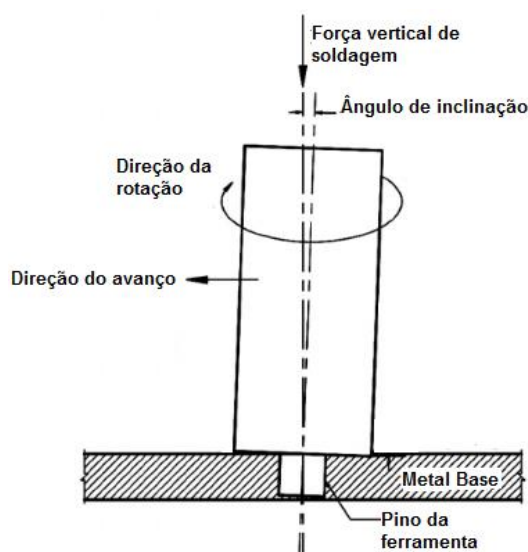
Ferramenta para soldagem FSW ilustrando a força vertical de soldagem e o ângulo de inclinação.
